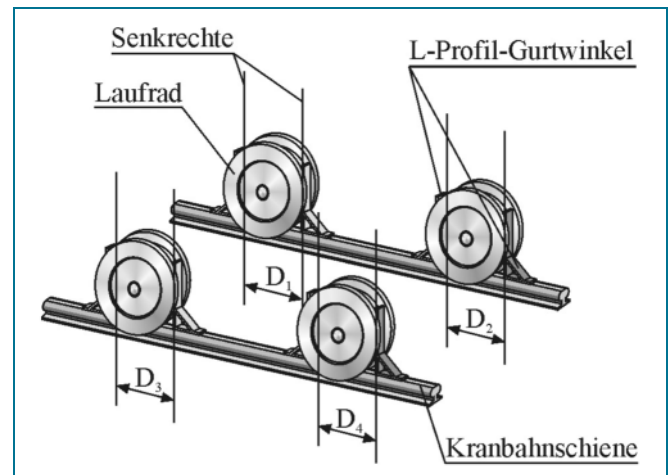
Bestimmung der Radkörper-Durchmesser der Laufflächen mit dem Grundrissverfahren
